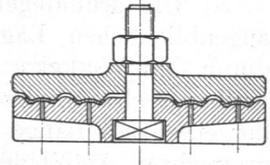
Presse für die Lederringe des Fernisventils Abb. 772. M. 1:10.
